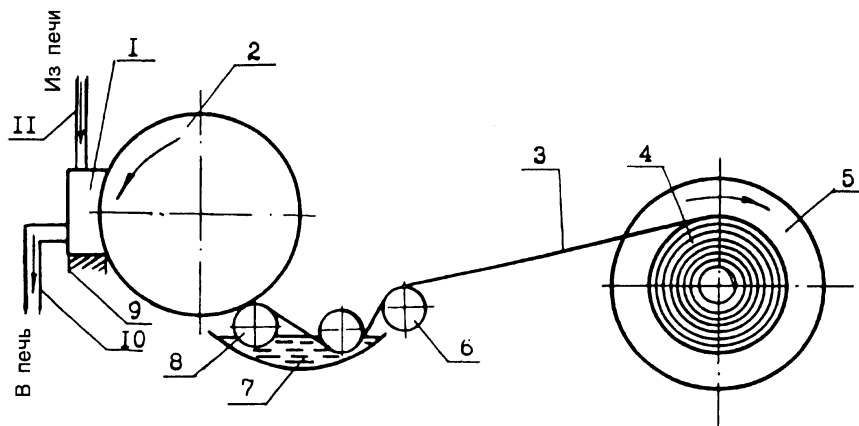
Схема непрерывного литья аккумуляторной решетки: 1 — башмак-питатель; 2 — формообразующий валок; 3 — решетчатая лента; 4 — рулон; 5 — шпуля; 6 — натяжной ролик; 7 — водяная ванна; 8 — контактный ролик; 9 — опора; 10 — сливной трубопровод; 11 — подающий трубопровод
